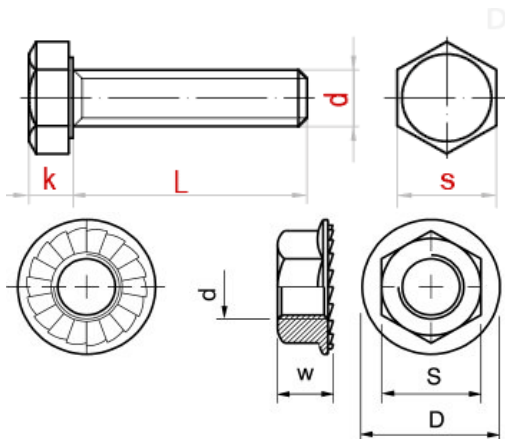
Болт с шестигранной головкой, полная резьба, высокопрочный, оцинкованный. Стандарт DIN 933 и гайка шестигранная с фланцем, высокопрочная, оцинкованная. Стандарт DIN 6923
